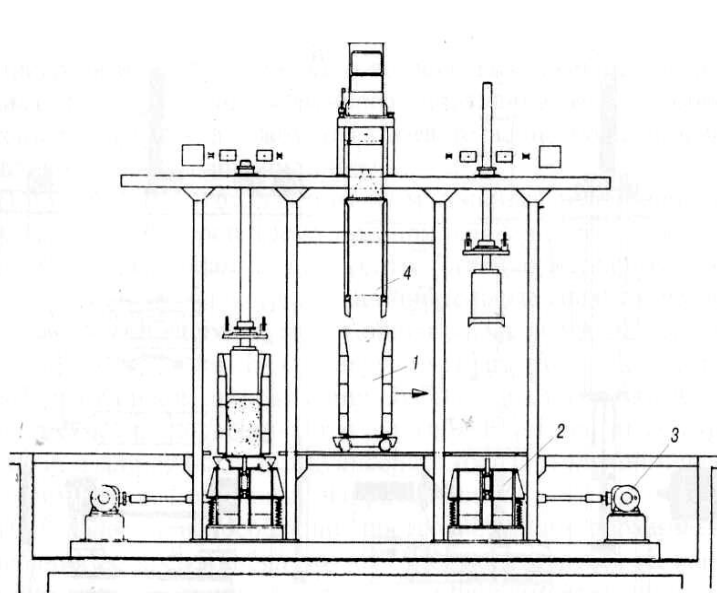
Вибромашина с двумя стационарно расположенными столами и передвижными виброформами: 1 - передвижная виброформа; 2- вибростол; 3- привод вибростола; 4- взвешивающий кубель.
